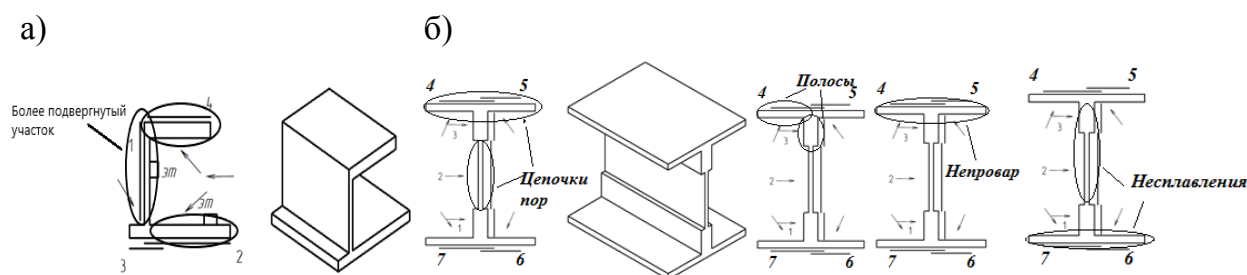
Места расположения дефектов в сварном соединении изделий: а – из сплава ВТ20; б – из сплава ВТ23
